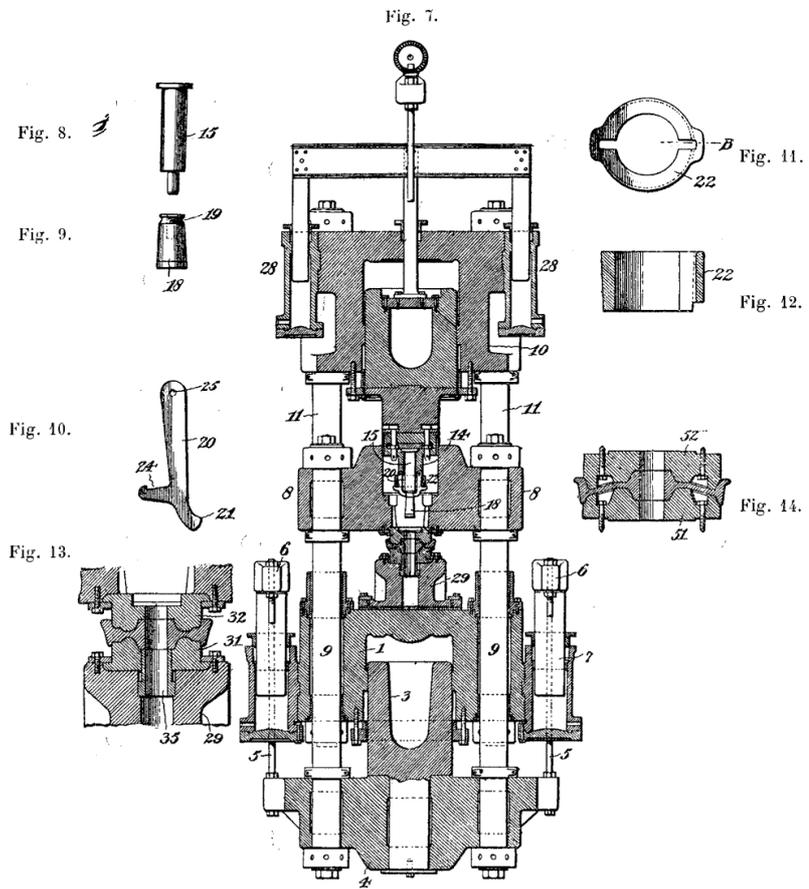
à 14. — Presse Loss. Coupe verticale et détails.
